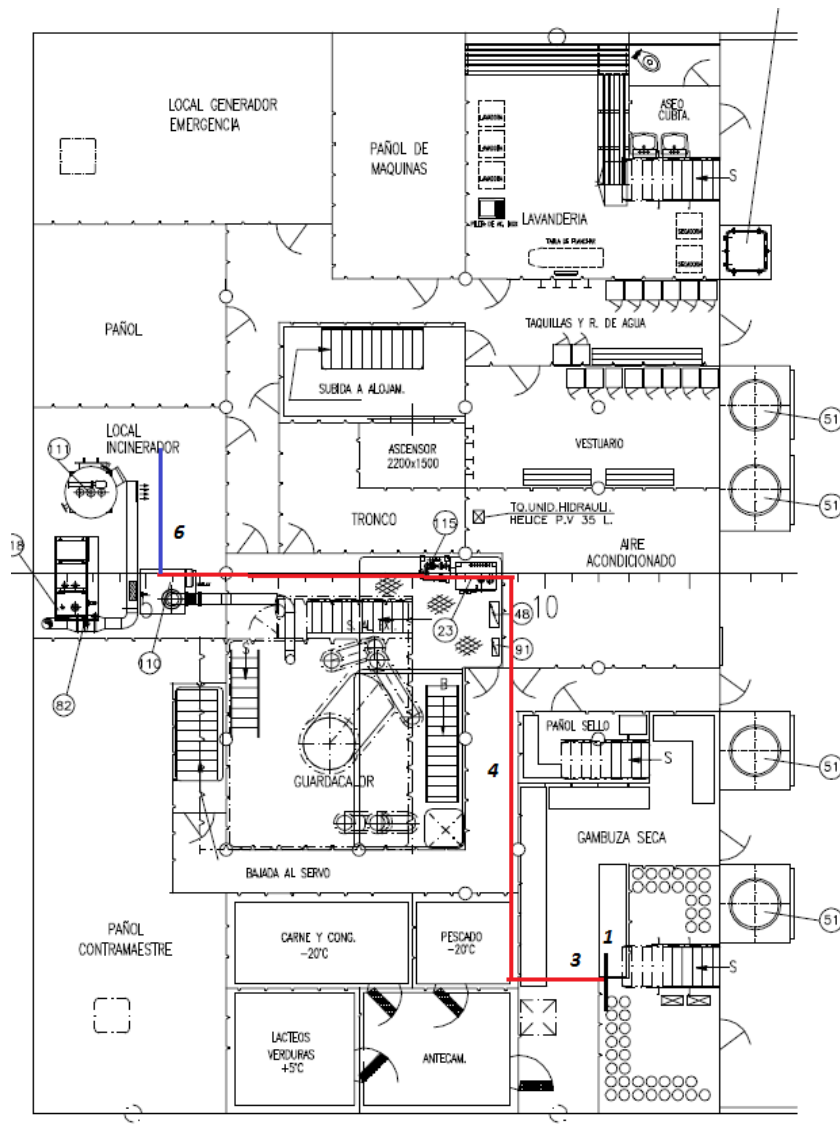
Planta de la Cubierta Principal del Verónica B
